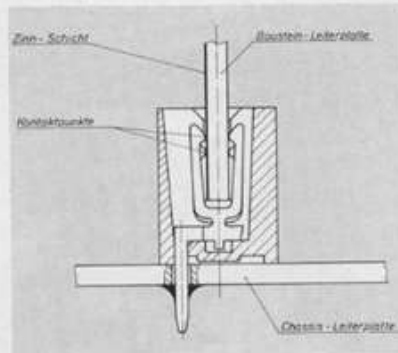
Ausführung der Kontaktfeder mit zwei Druckauflagepunkten
